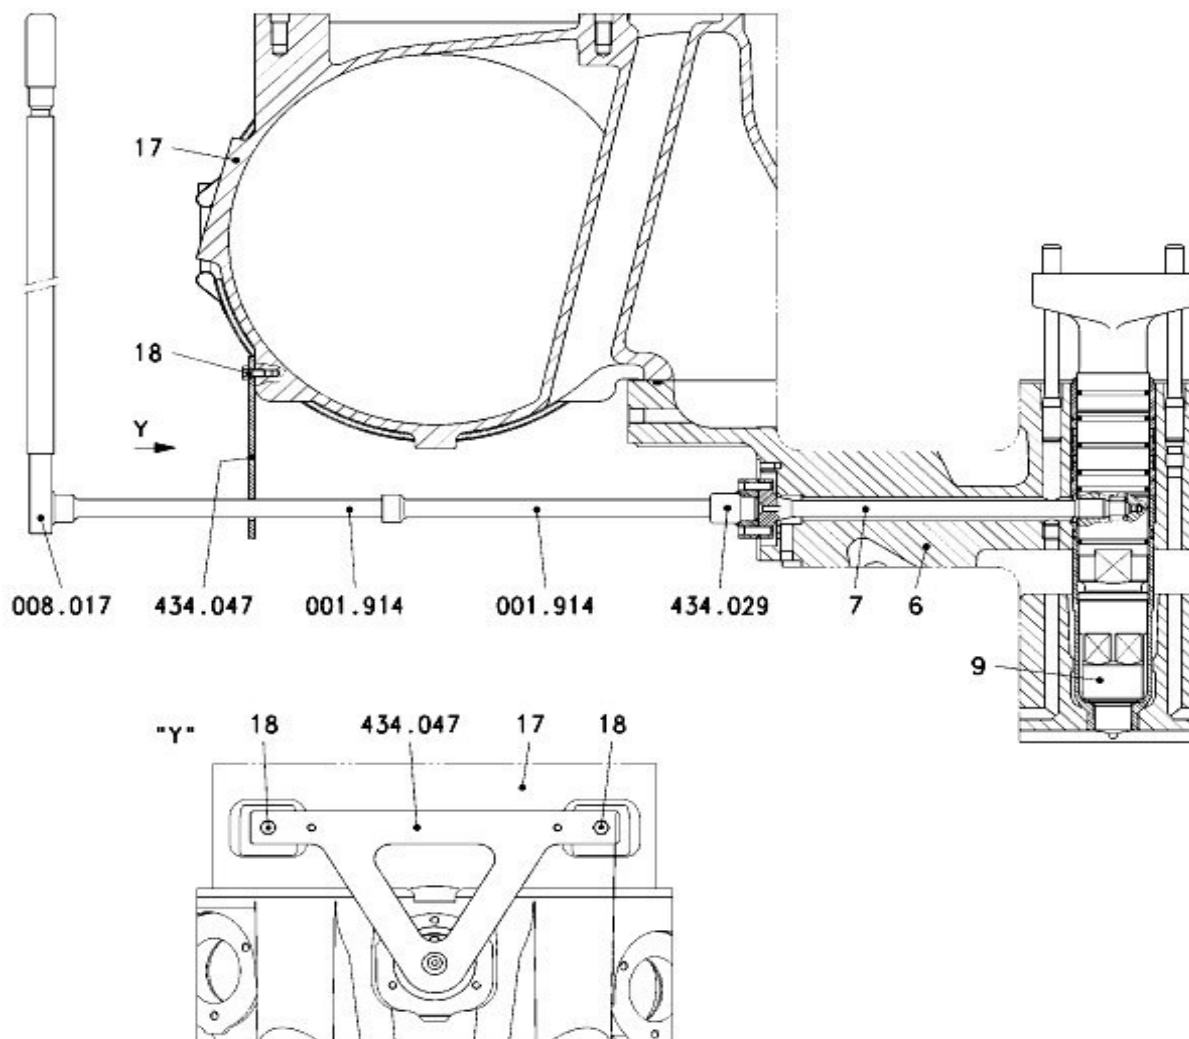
Розкручування / затягування шестигранної гайки - показано затягування гайки: 6 - головка циліндра; 7 - різбовий елемент; 9 – паливна форсунка; 17 - кожух рукоятки; 18 - шестиграний болт М10х20
